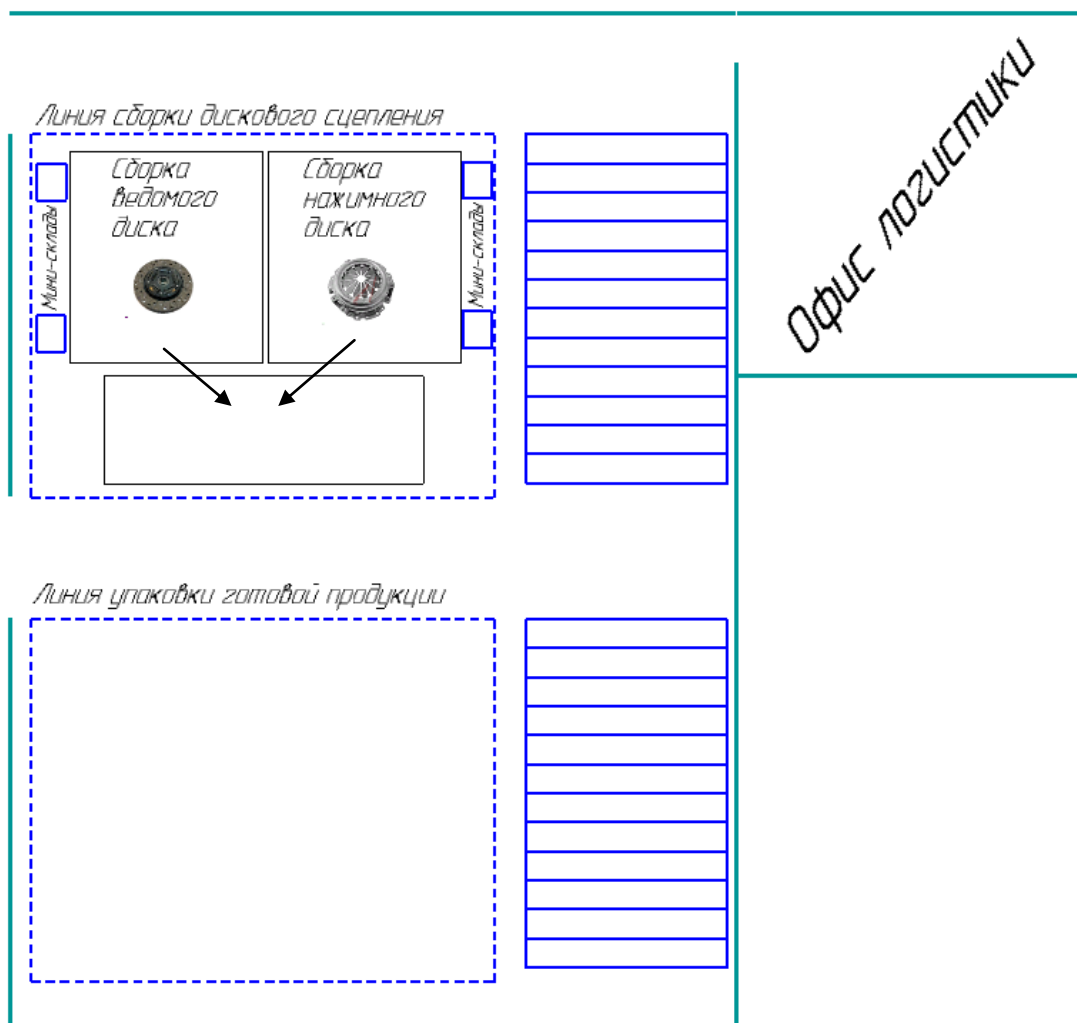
Схема зоны сборки и упаковки дисковых сцеплений
